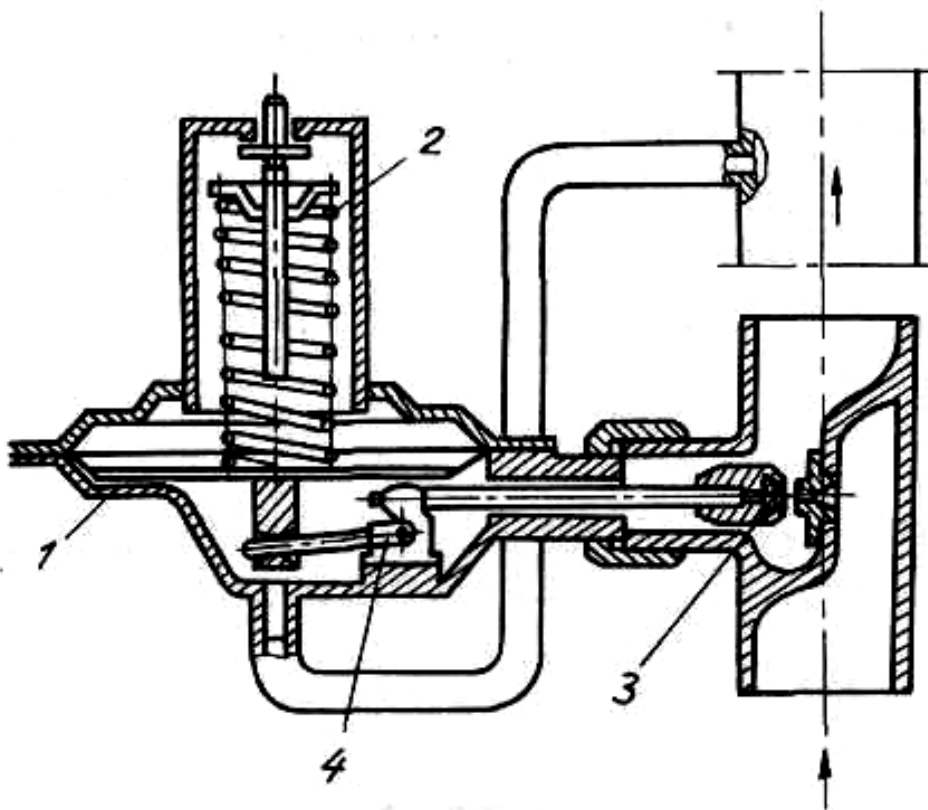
Принципиальная схема регулятора давления с рычажной передачей: 1 – рабочая мембрана; 2 – пружина настройки; 3 – рабочий клапан; 4 – рычажная передача.
